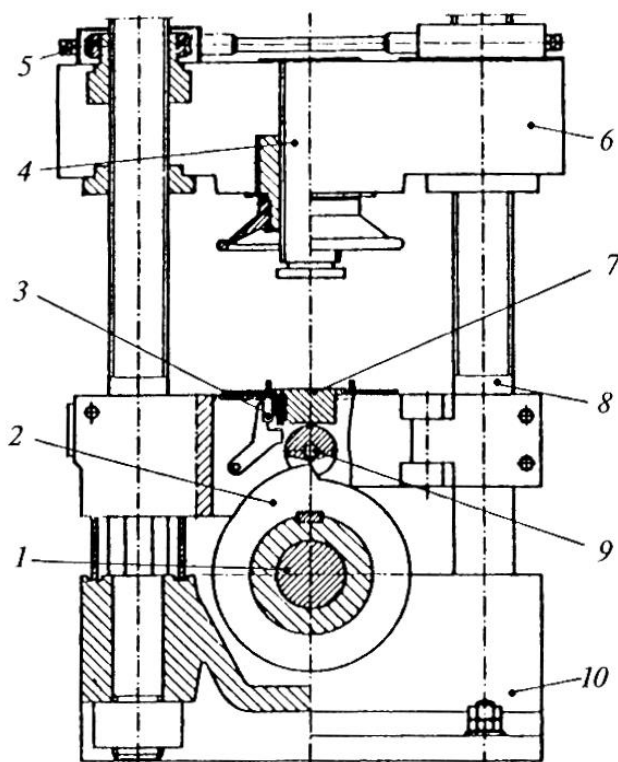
Схема кулачкового пластометра конструкции Бала –Чайка (Польша):
